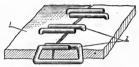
Подготовка тонкостенной детали к заварке трещины с двух сторон: 1 — деталь; 2 — гладкие шпильки.
